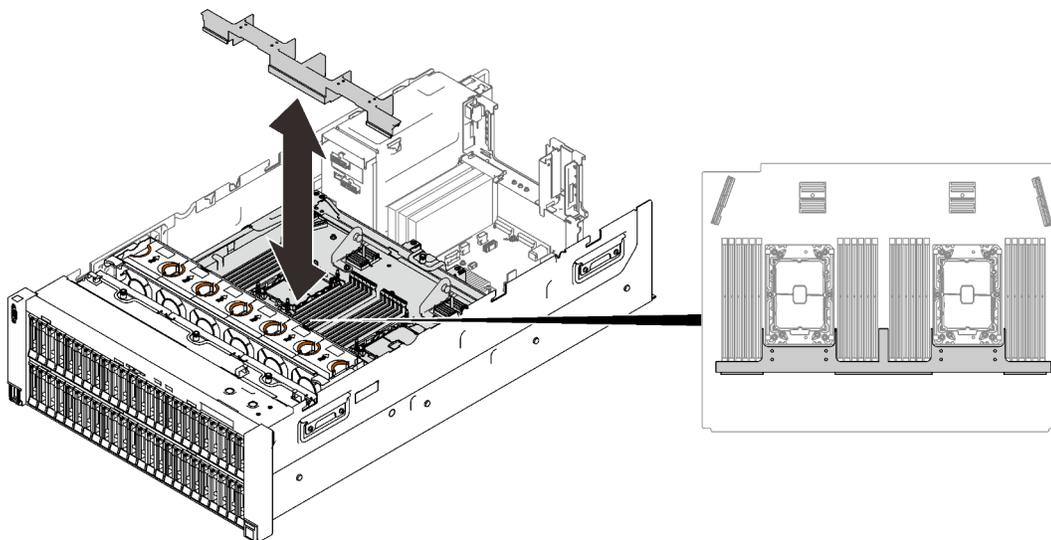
Installazione del deflettore d'aria sul vassoio di espansione
